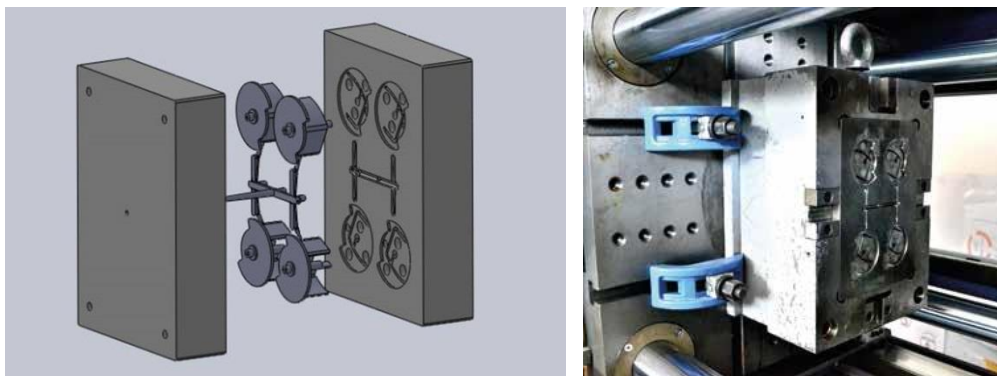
Molde utilizado en la experimentación a) Imagen de Auto-CAD b) Montado en máquina
